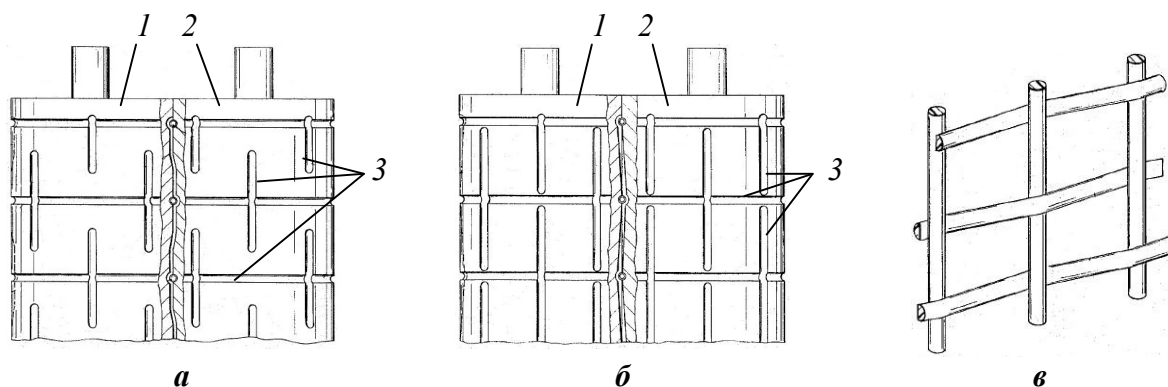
Формующий инструмент (а, б) способа получения плоских полимерных сеток (в) заполнением расплавом рельефного узора на поверхностях двух встречно вращающихся цилиндров: 1, 2 – валки; 3 – пазы на поверхностях валков
